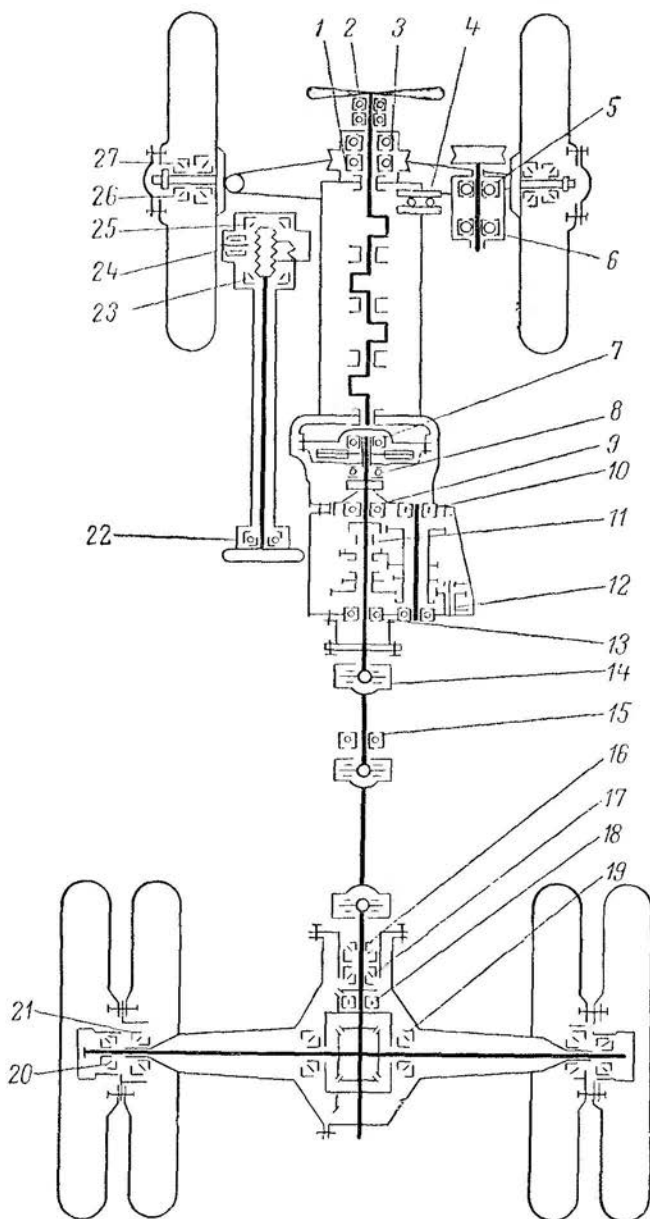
Схема расположения подшипников автомобиля ГАЗ-53А
